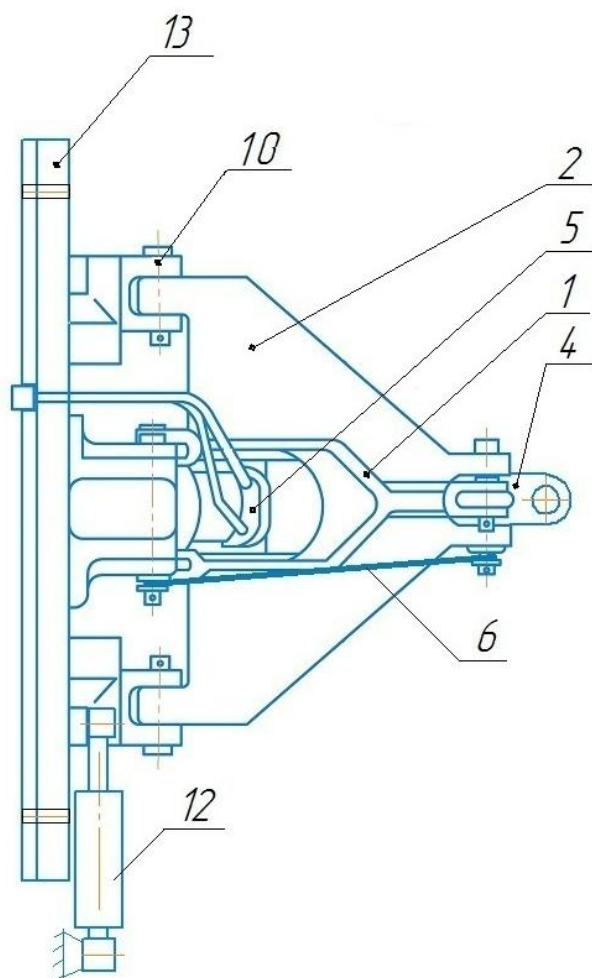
Прицепное устройство трактора (вид сверху)
